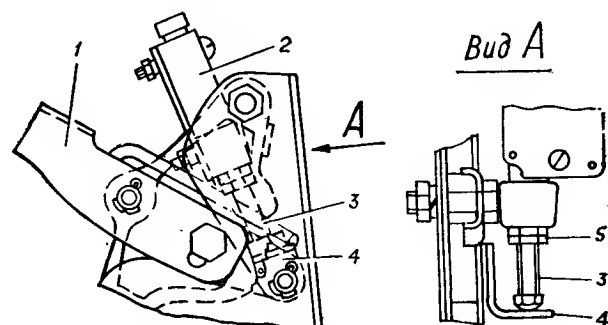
Установка конечного выключателя контрольной лампы стояночного тормоза:
